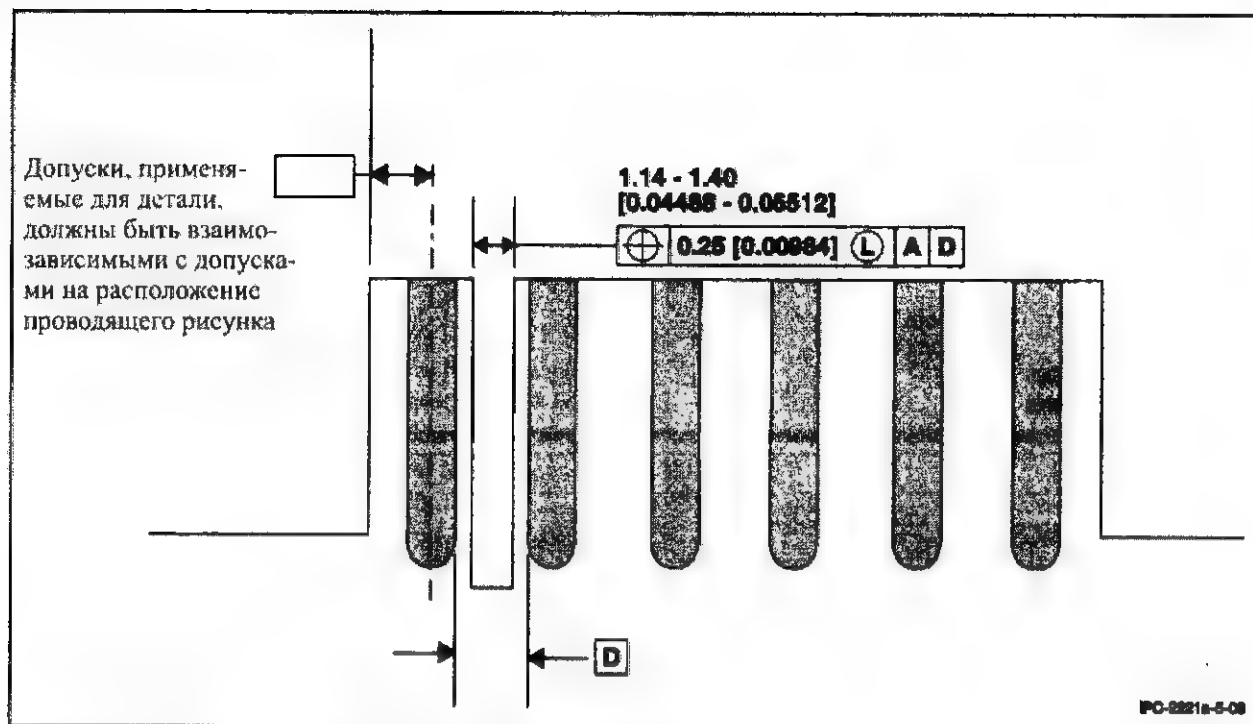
Пример расположения и допуска ключевого паза разъема, мм
